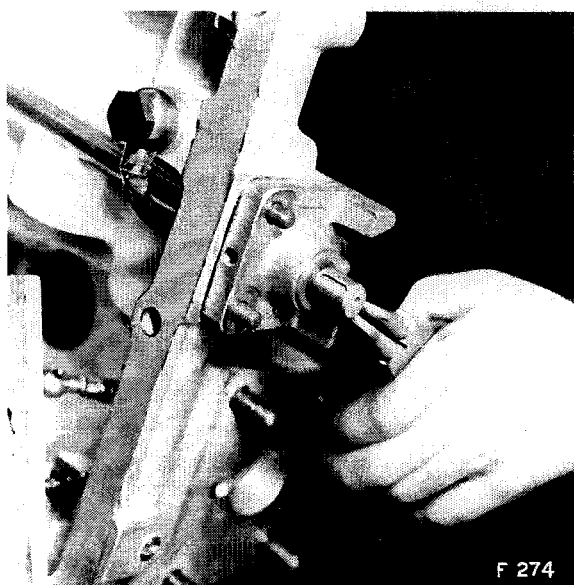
Ausbau des Kolbens N/S und der gelösten Schraube für die Schaltachs-Arretierung
